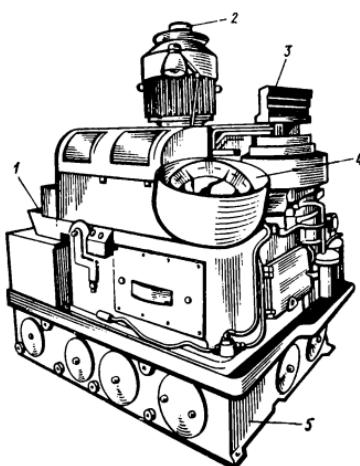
Непрерывно-протяжной автомат ТГ-1 с поворотным столом:
